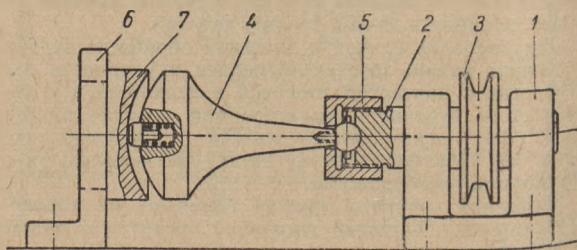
Приспособление для притирки сферической поверхности контрольного клапана:
